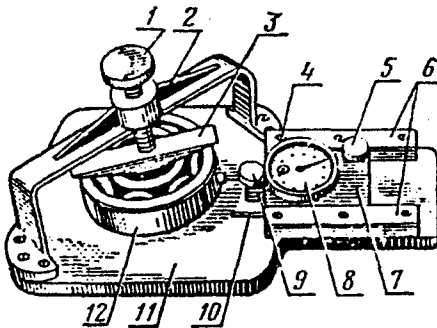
Индикаторный прибор Ки-1223 для проверки радиальных зазоров в подшипниках качения: размер А шаблона равен допустимой без ремонта толщине зуба, а размер Б — нормальной высоте головки зуба. При наличии зазора С между вершиной зуба и шаблоном шаблон пригодна для дальнейшей работы. Определение рационального зазора в подшипниках качения представлено на рис. 4.14.
